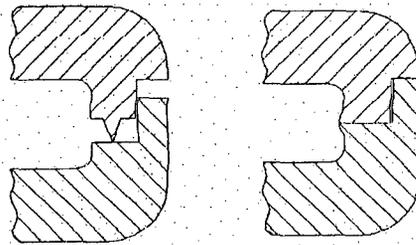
União de encaixe para soldagem ultrassônica.
